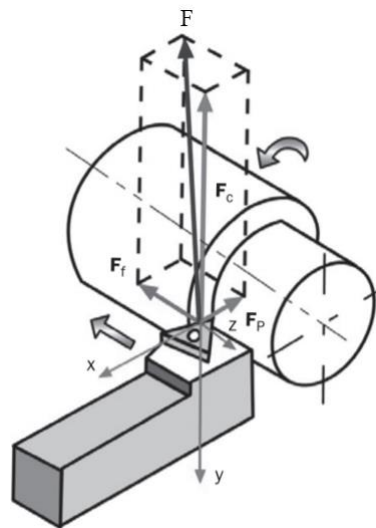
Componentes da força de usinagem no torneamento.
